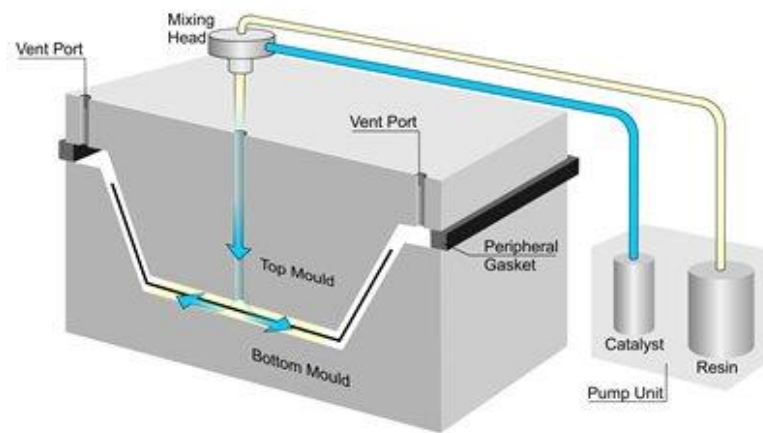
Método de fabricação por Moldagem por Transferência de Resina-RTM
